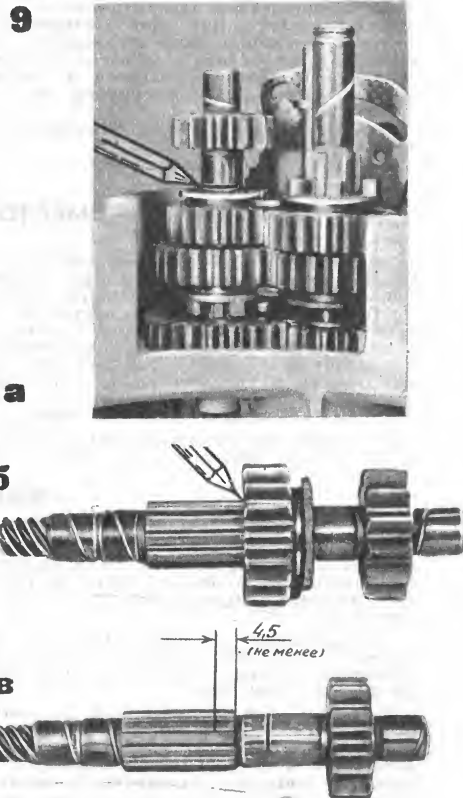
Определение глубины, на которую шестерня третьей передачи села на зубья промежуточного вала: а — первая отметка; б — вторая отметка; в — расстояние от края зуба до второй отметки.
